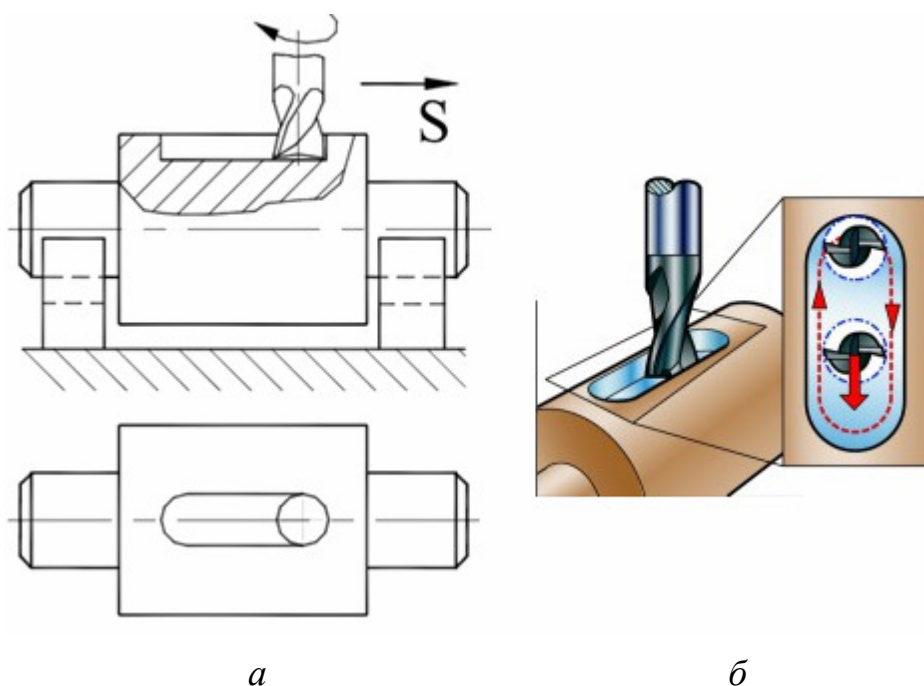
Примеры схем обработки пазов: *а* – черновое фрезерование на полную ширину паза; *б* – фрезерование паза за 2 прохода
